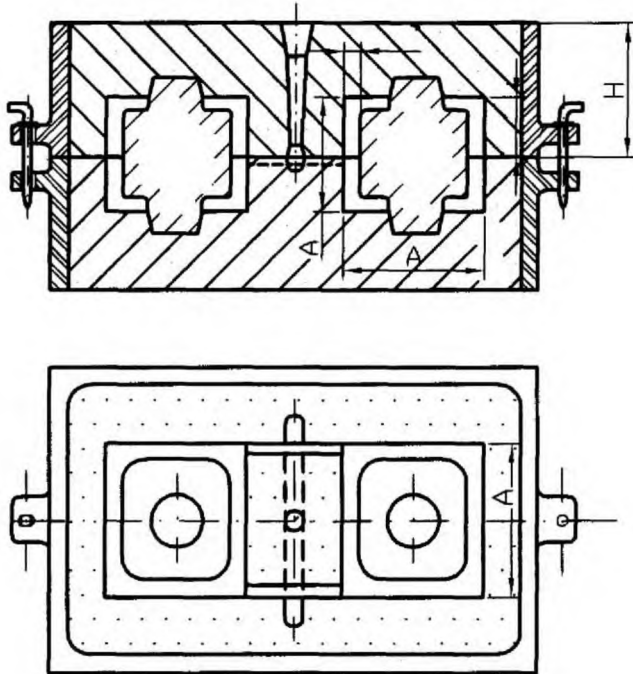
Основные размеры отливки и ее положение в литейной форме
